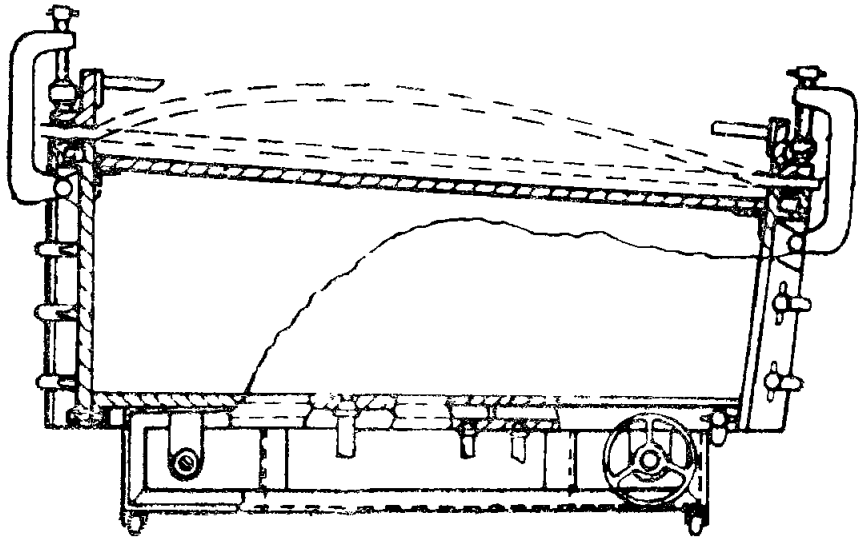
Схема и приспособление для пневмоформования второй стадии сложных деталей:
